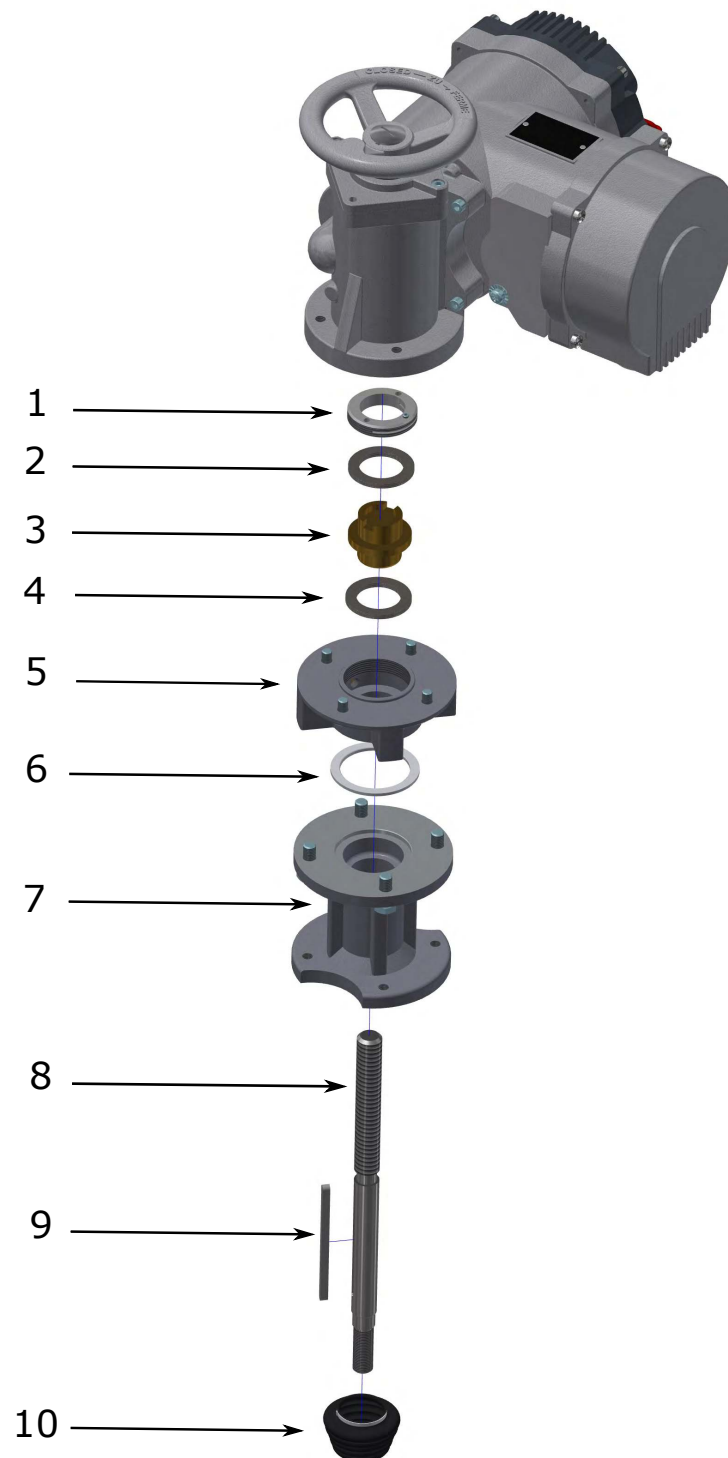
1... Ringmutter, 2... Axiallager, 3... Spindelmutter, 4... Axiallager, 5... Abtriebsflansch, 6... Zentrierring, 7... Gehäuse Schubeinheit, 8... Spindel, 9... Führungspassfeder, 10... Faltenbalg
